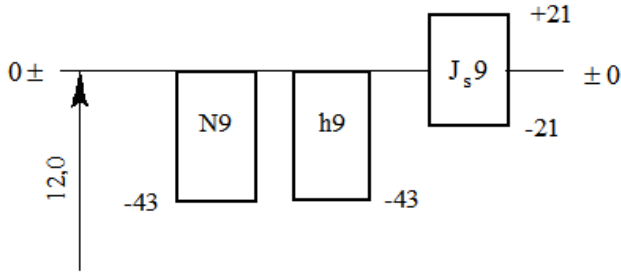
Схема полей допусков шпоночного соединения
